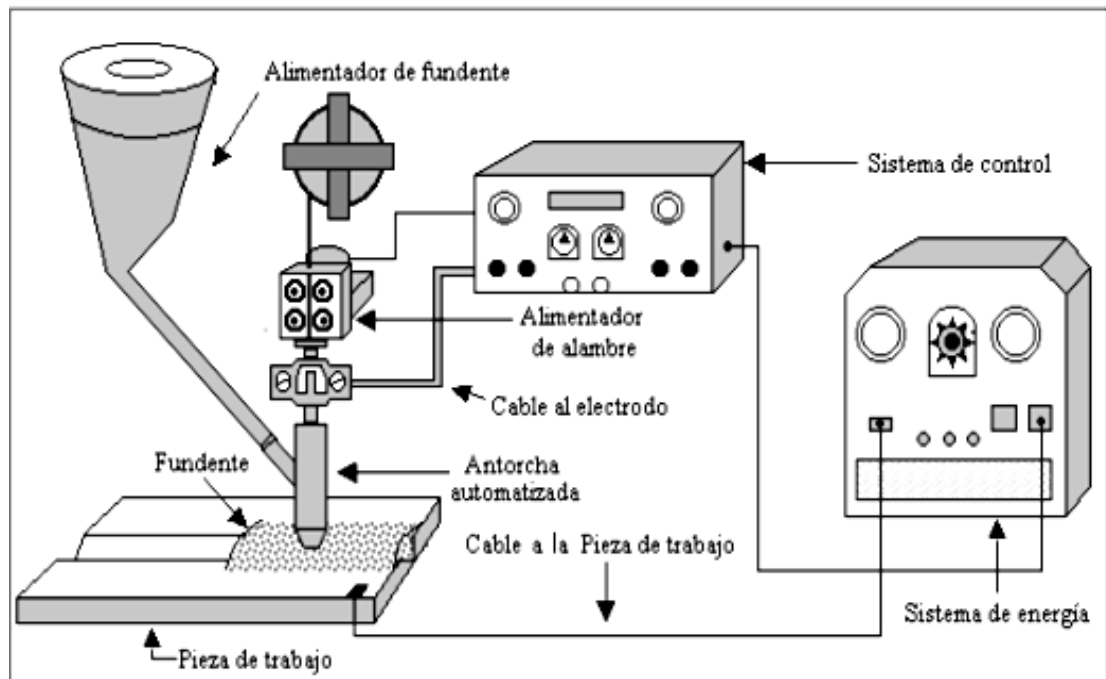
EQUIPO DE SOLDADURA PARA EL PROCESO SAW
